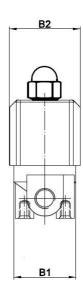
Размеры клапанов Ду6-8 корпус латунь
